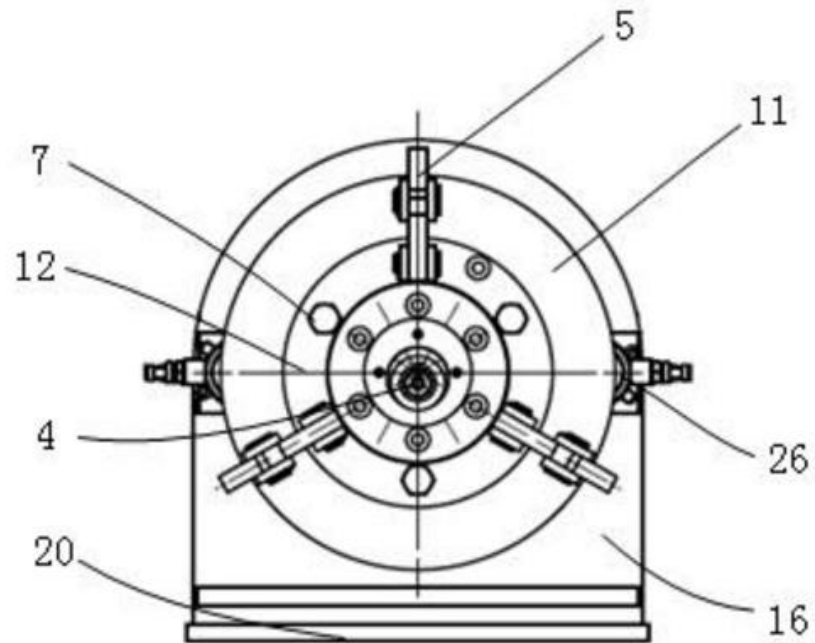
Пристрій для приєднання до колеса, поперечний переріз В-В
